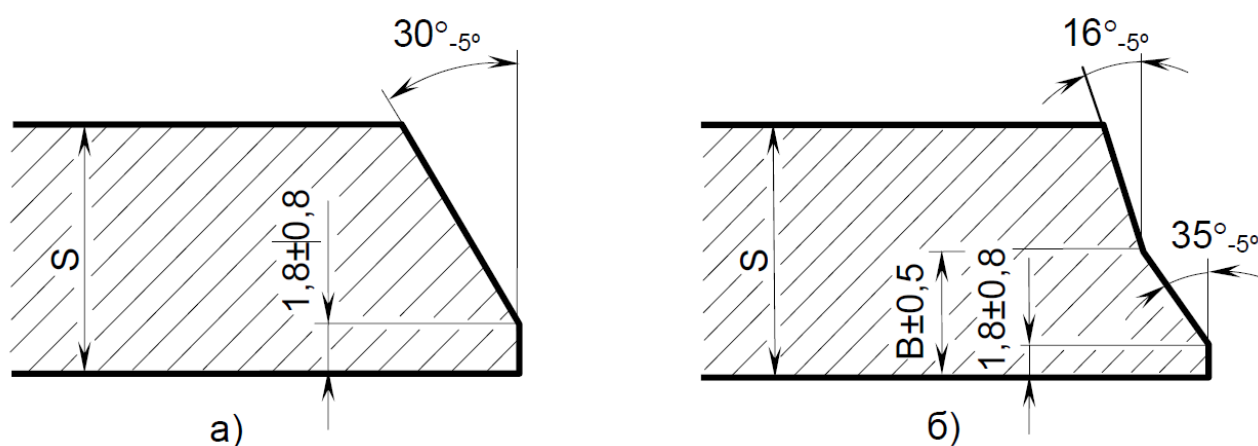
Геометрические параметры заводской разделки кромок торцов труб для сборки под сварку
